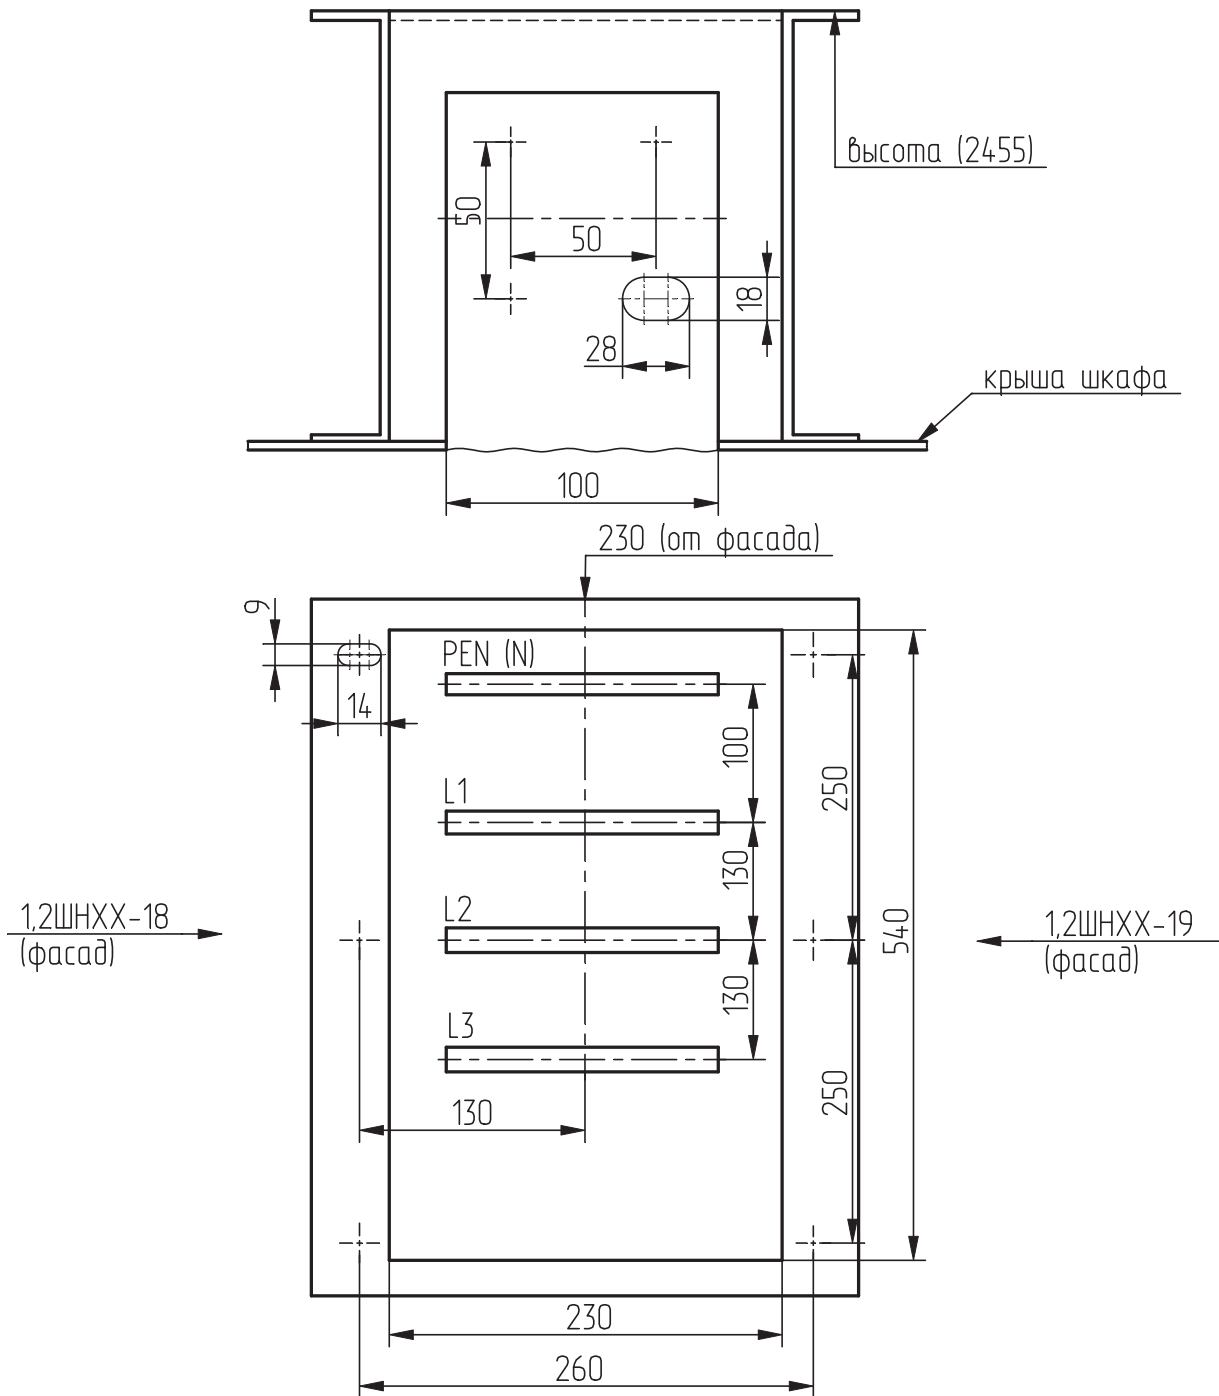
Присоединительные размеры для установки шинопроводов на номинальный ток 1000 и 1600 А
